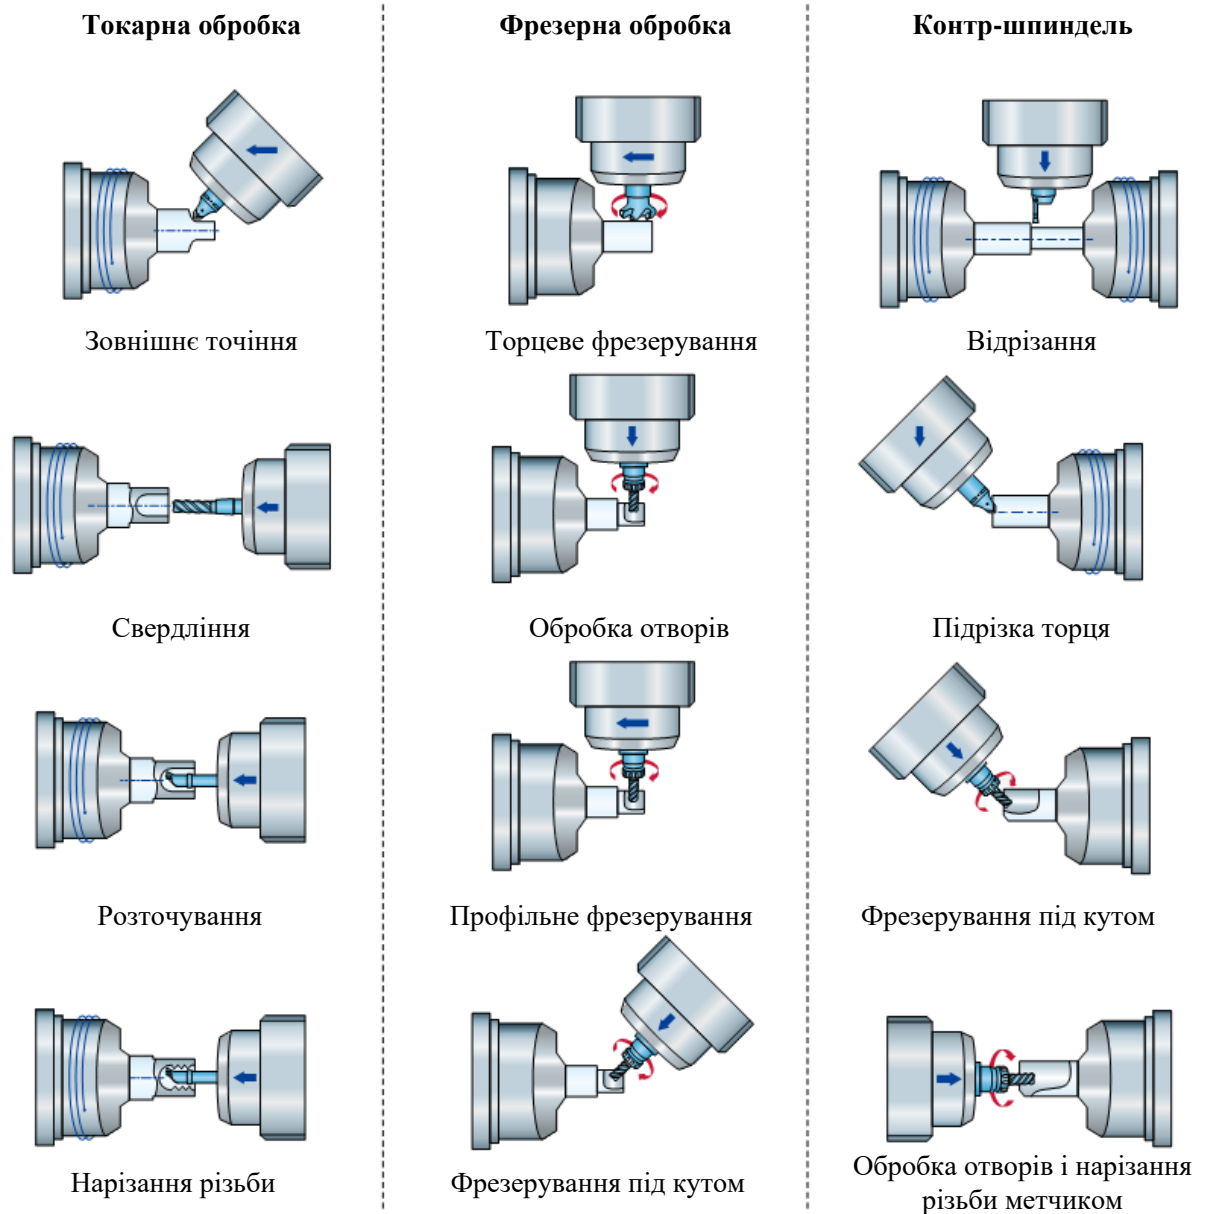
Варіанти обробки деталей на верстаті PUMA MX1600
